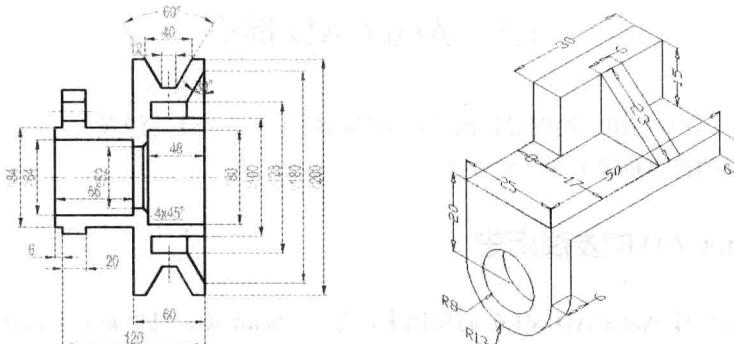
利用 AutoCAD 标注的平面图形和三维图形
